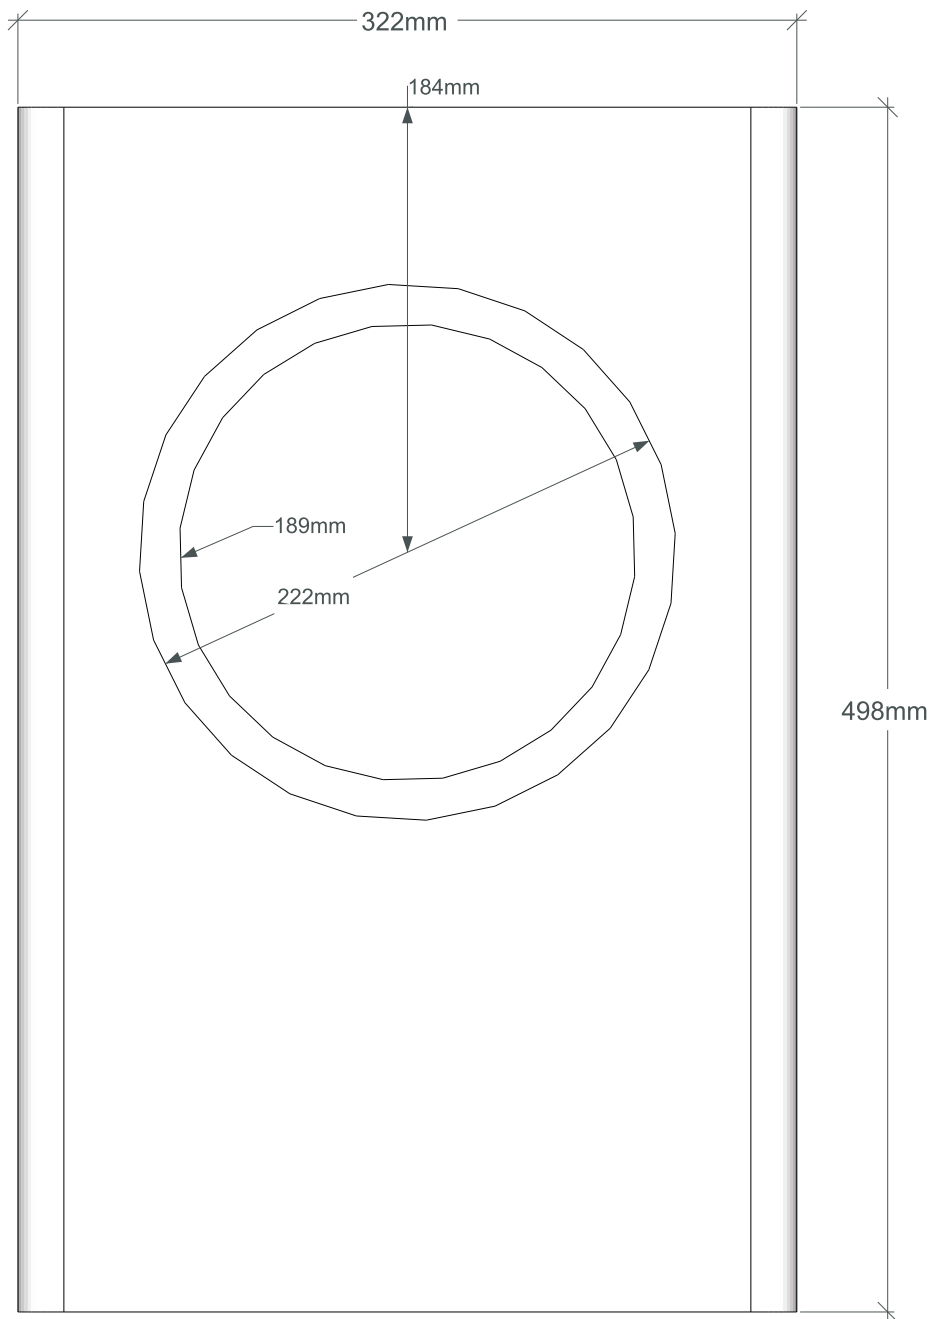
Frontansicht geschlossenes 22,9l Gehäuse
